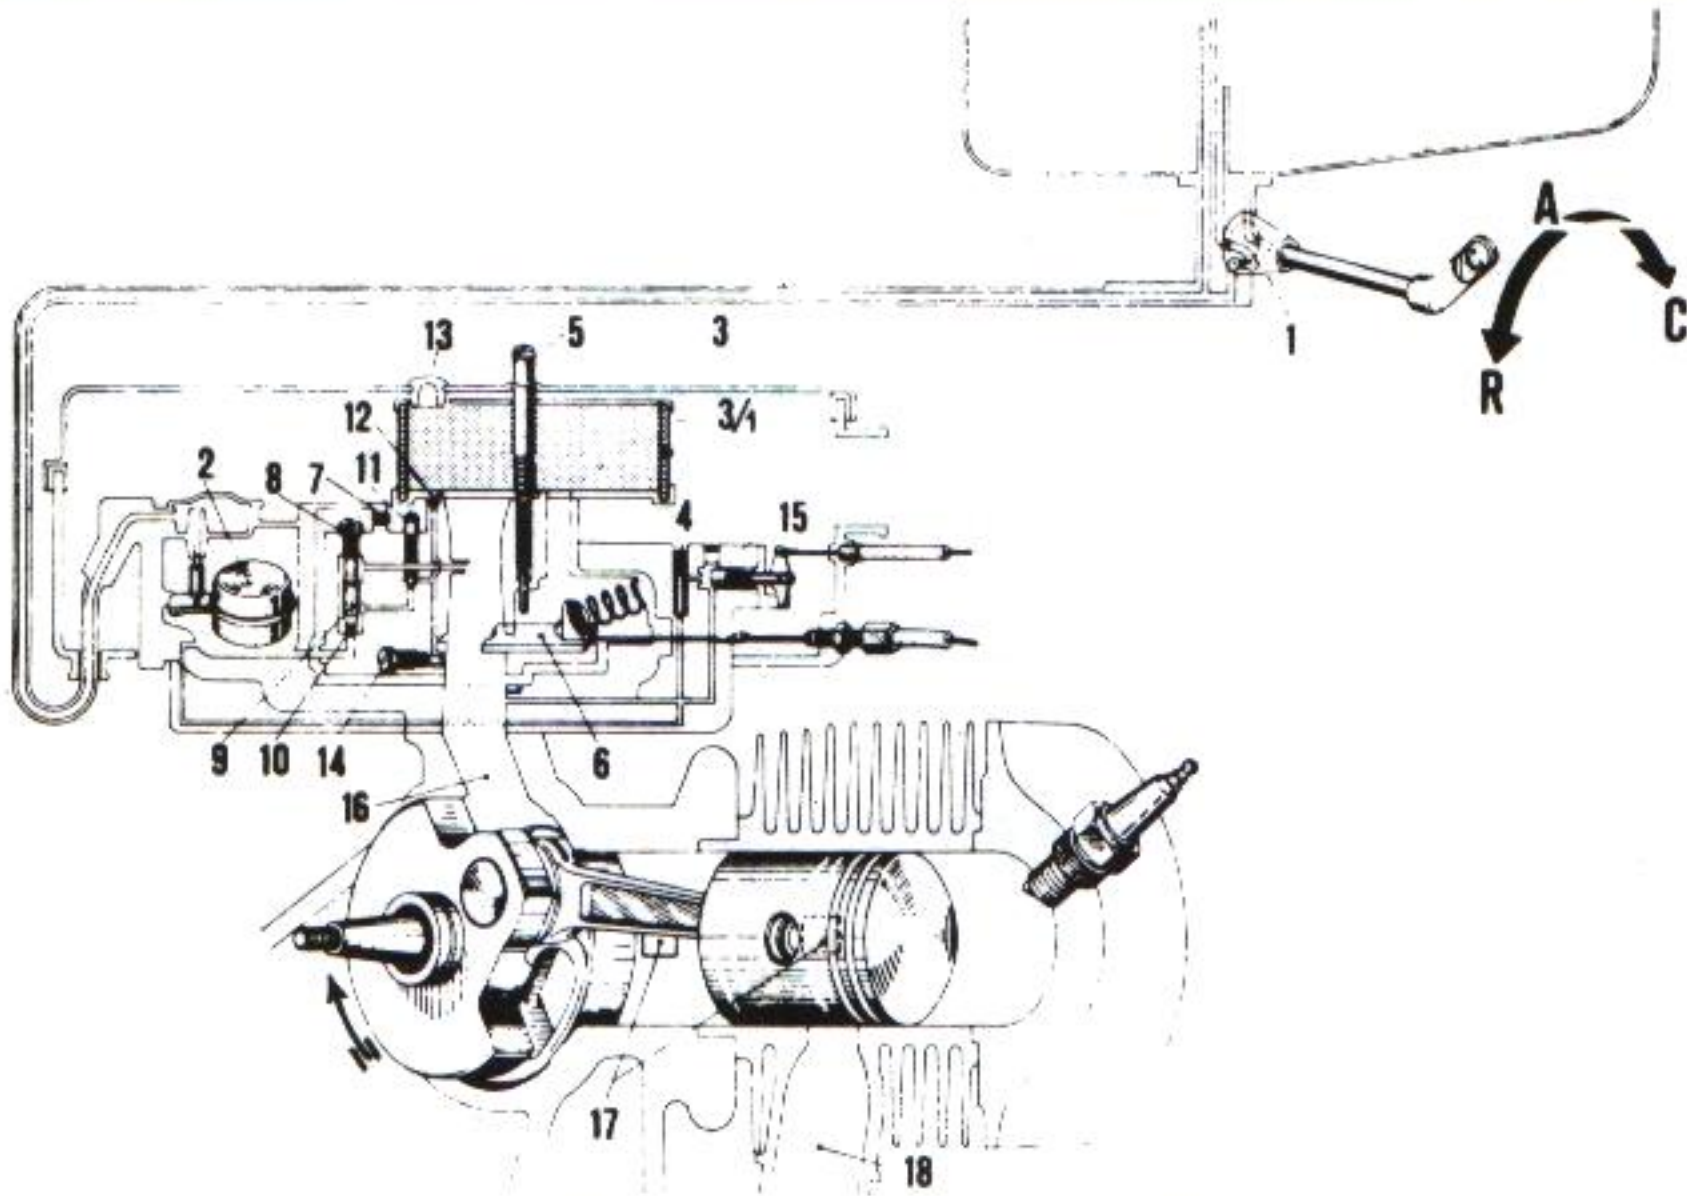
Esquema de un carburador de la marca DELL'ORTO para el escúter VESPA.
